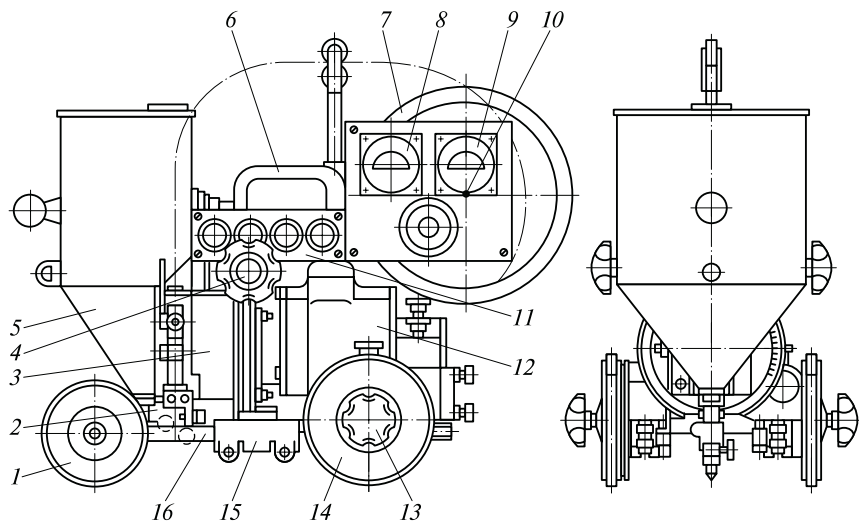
Сварочный трактор АДФ-1002:
